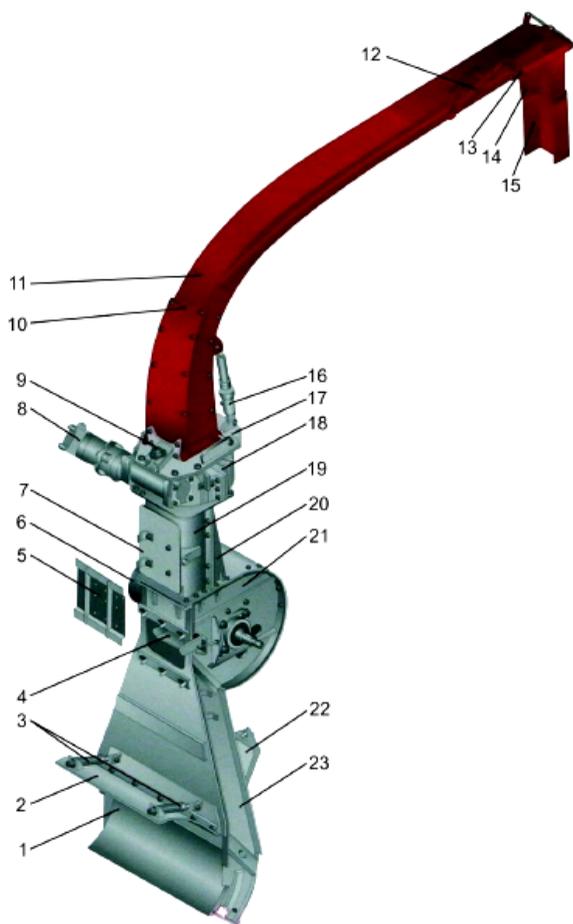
Транспортирующее устройство: 1 – вставка (направитель потока массы); 2 – крышка измельчающего аппарата; 3 – пружины прижимные; 4 – лопасть ротора ускорителя массы; 5 – крышка ротора ускорителя; 6 – шкив привода ротора ускорителя; 7 – защитный щиток; 8 – гидромотор привода поворотного устройства силосопровода; 9 – болт откидной; 10 – накладка силосопровода (сменная); 11 – силосопровод; 12 – гидроцилиндр поворота козырька силосопровода; 13 – рычаг поворота козырька; 14 – козырек силосопровода; 15 – надставка козырька; 16 – гидроцилиндр подъема силосопровода; 17 – опора силосопровода; 18 – поворотное устройство силосопровода; 19 – переходник; 20 – сектор; 21 – корпус ускорителя; 22 – крышка смотрового люка; 23 – конфузор
